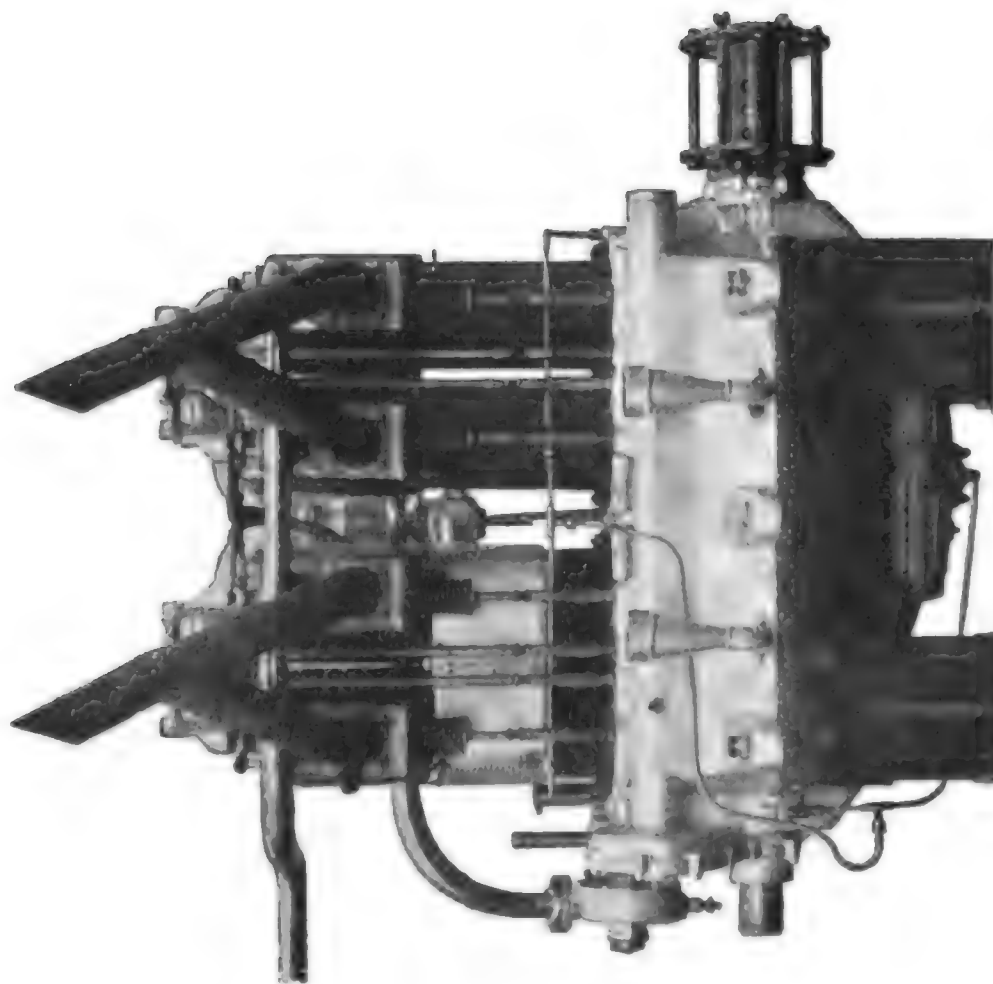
100 PS Dixi-Flugmotor. Auspuffseite
